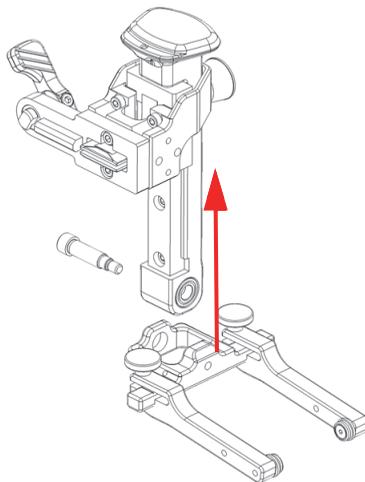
Выдвижение направляющей подпружиненного рычага из стержня вилки
